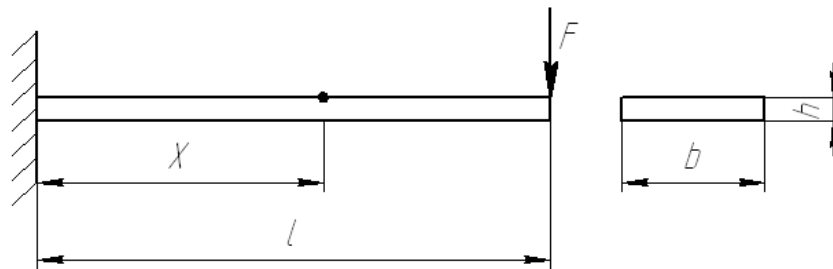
Розрахункова схема деформація балочного пружного перетворювача
